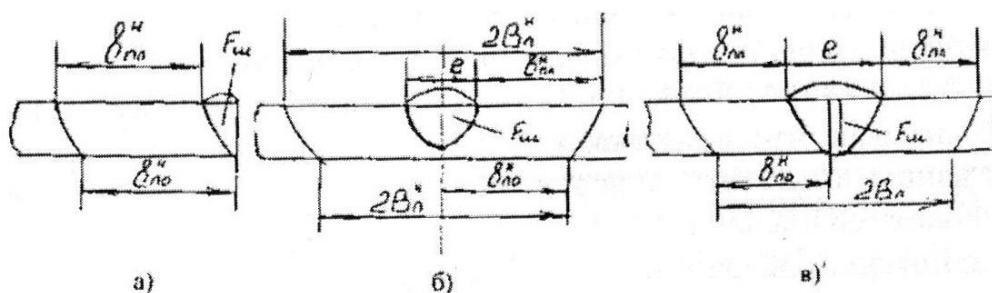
Формування активної зони у різних типів зварних з'єднань: а – наплавка на крайку; б – наплавка на лист; в – зварювання в стик.
